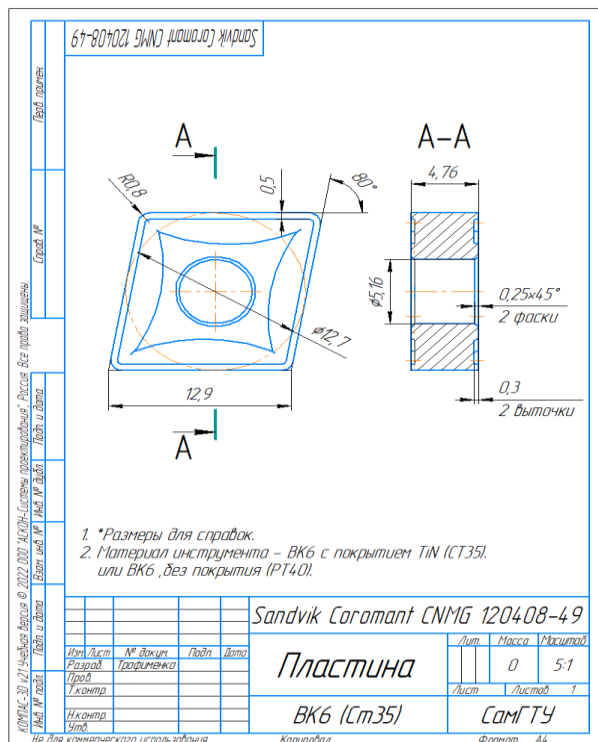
Рабочий чертеж СМП, полученный путем реверсивного инжиниринга
